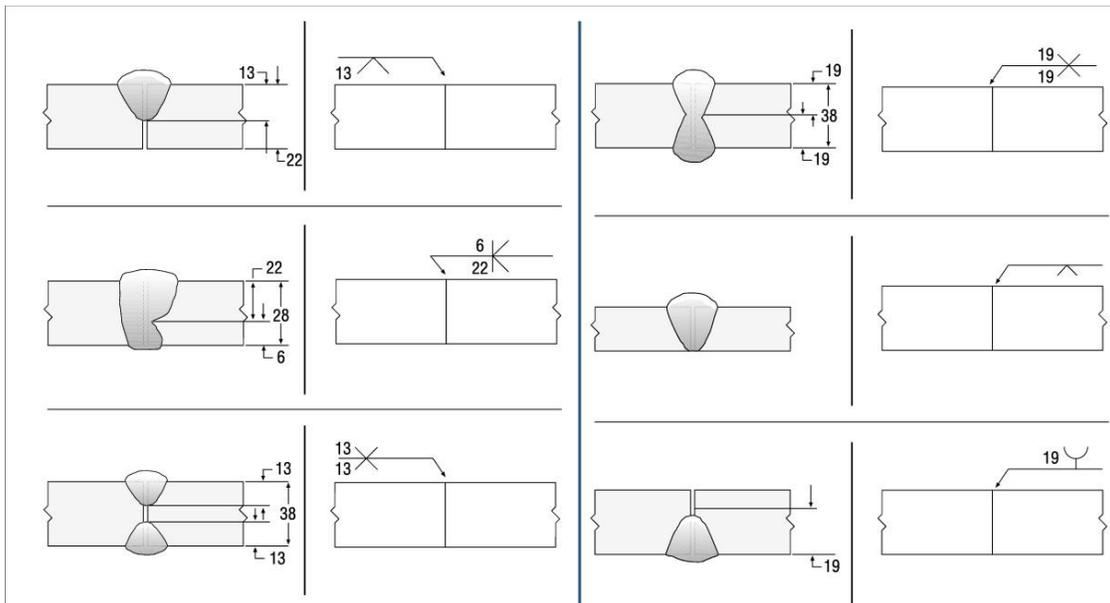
Ejemplo de simbología para soldaduras a tope.
